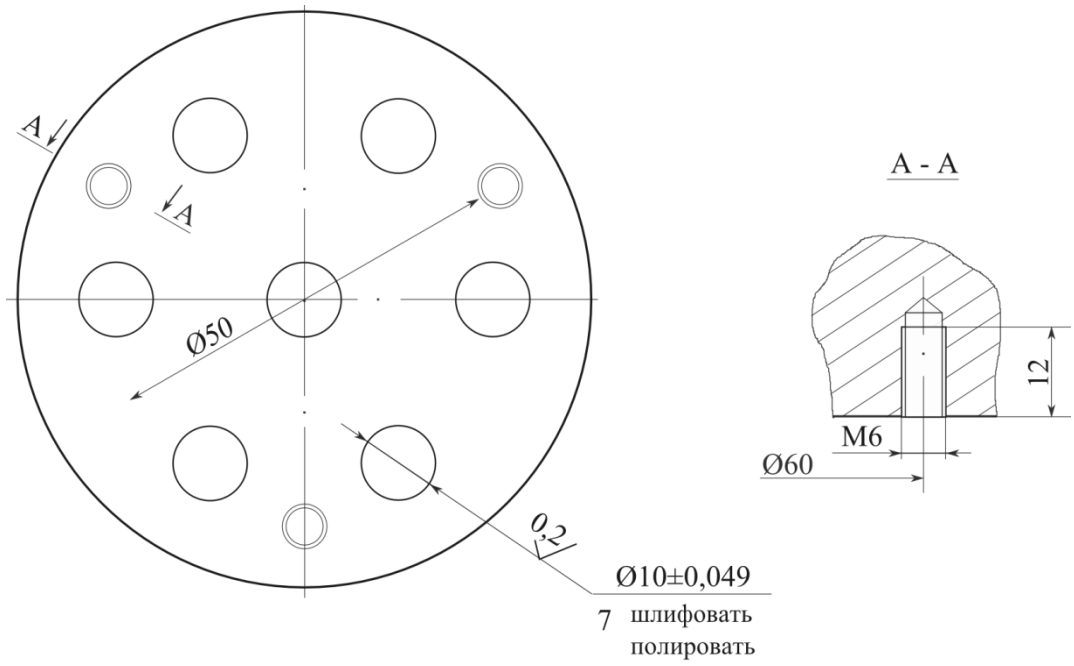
Многоместная пресс-форма для горячего прессования алмазосодержащих полиолефинов
